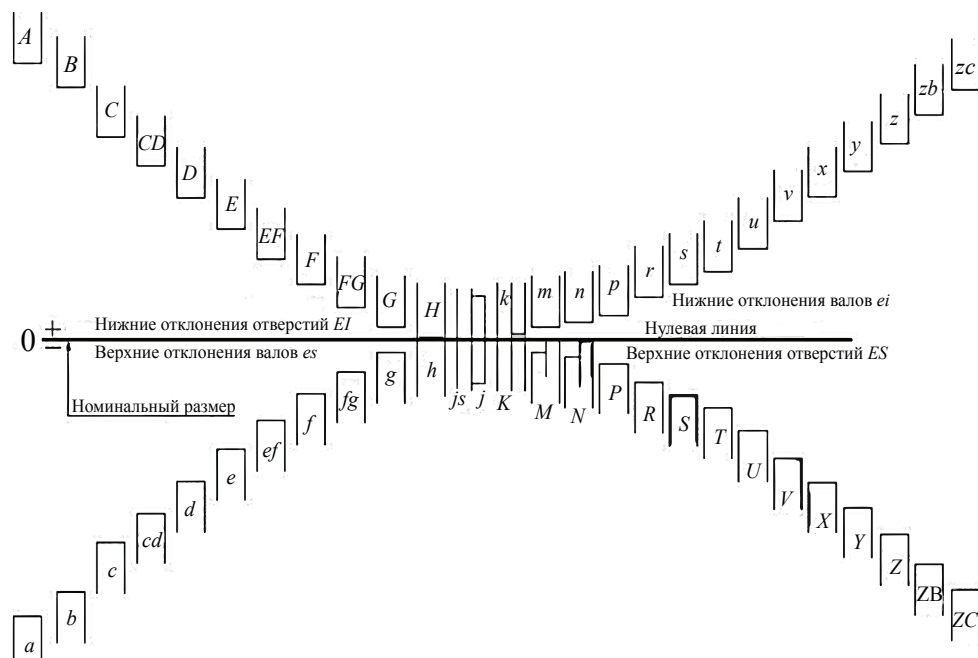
Расположение полей допуска для валов и отверстий
